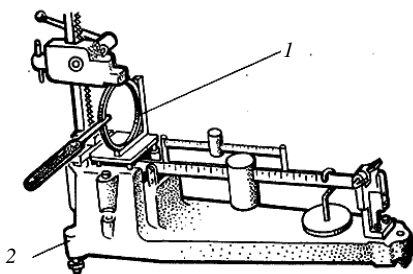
Проверка упругости поршневых колец: 1 – поршневое кольцо; 2 – приспособление КИ-0507-В
